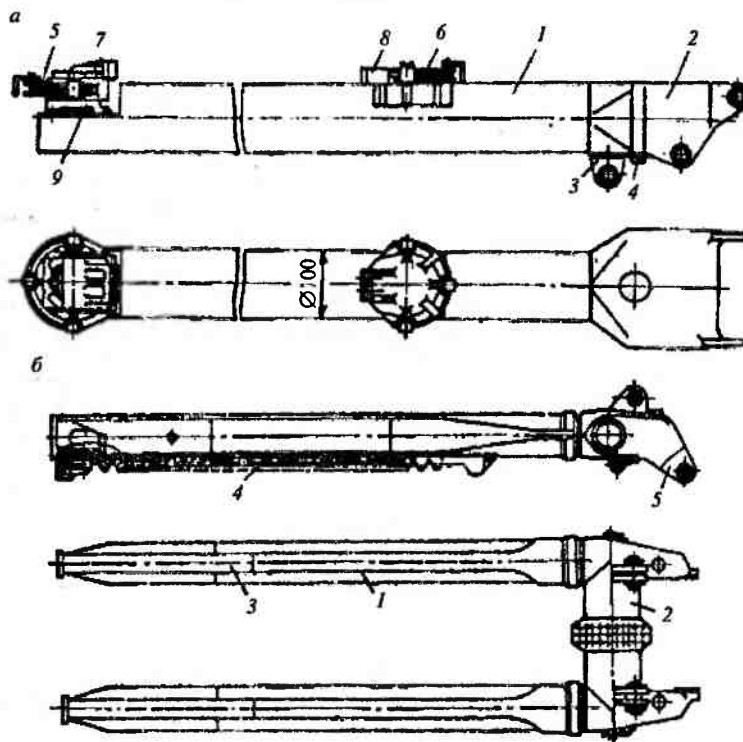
Рукояти одноковшовых экскаваторов:
